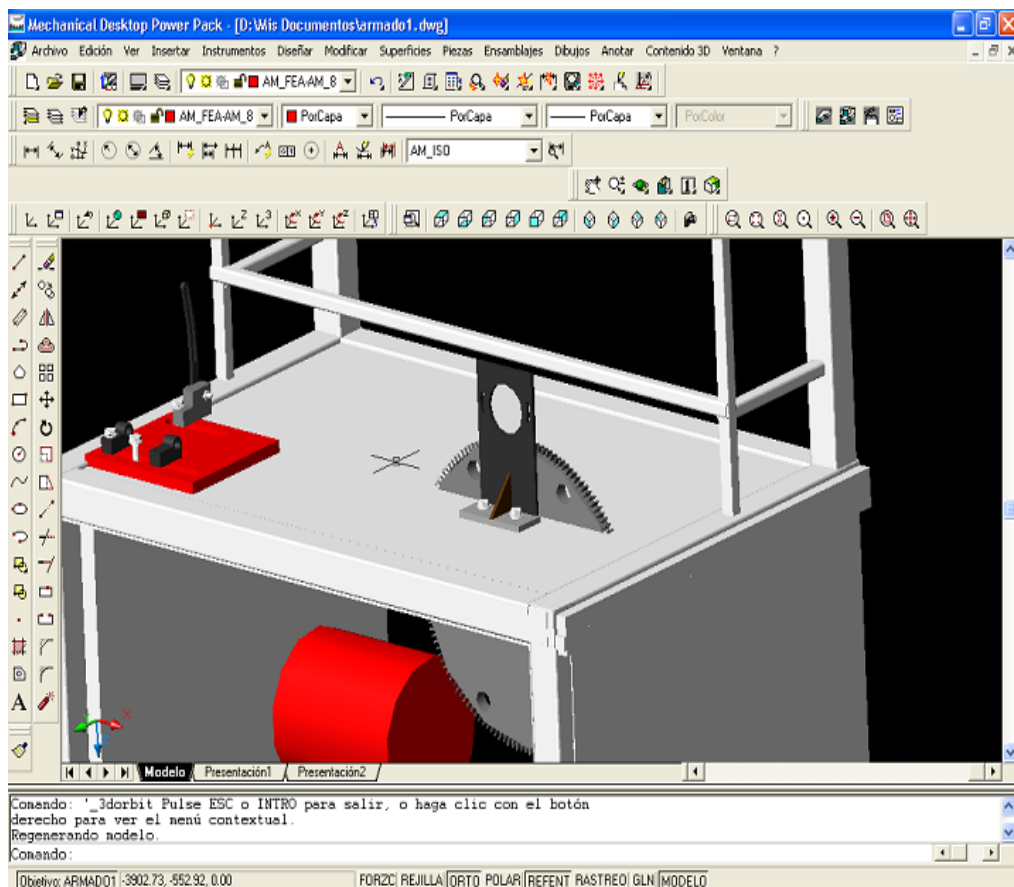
Montaje de las placas y rueda dentada en el banco comprobador
